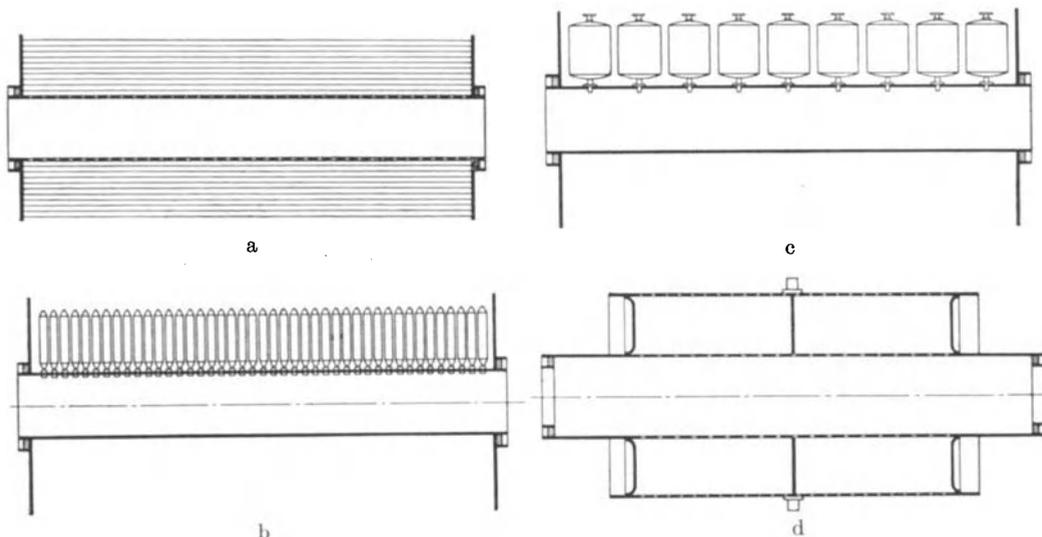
a—d. a Färbebaum für Ketten; b Aufsteckzylinder für Cops; c Aufsteckzylinder für Kreuzspulen; d Packzylinder für loses Material, Kardenband, Garn u. dgl.
